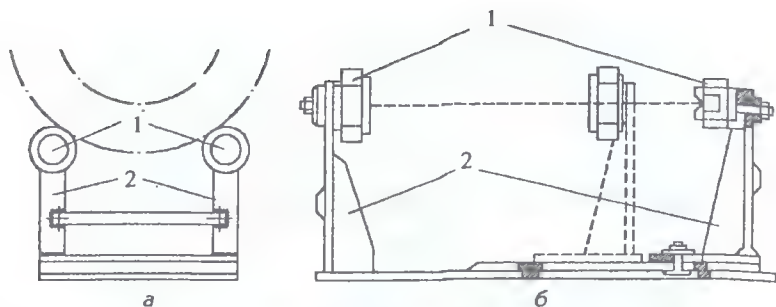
Принципиальные схемы приспособлений для поворота статора (а) или ротора (б) вокруг горизонтальной оси: 1 — подшипники; 2 — станина
